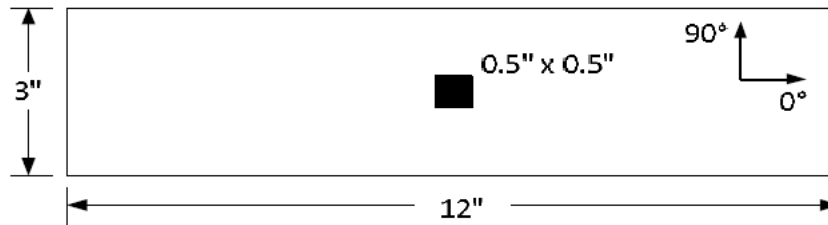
Géométrie et dimensions de l'éprouvette utilisée
